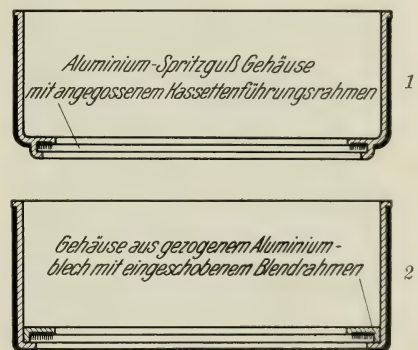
Ausführungsformen des Kameragehäuses mit ringsherumlaufenden Schutzkanten für die Beledung. 1. Eine sehr solide Gestaltung des Gehäuses läßt sich bei einem Minimum von Materialaufwand dadurch erzielen, daß man Aluminium-Spritzguß verwendet; trotz der geringen Wandstärke von 1,5 bis 2 mm ist die Festigkeit eine große und eine Nachbearbeitung der untereinander völlig gleichartigen Stücke überflüssig. 2. Gehäuse für Kameras in niedriger Preislage werden häufig aus dünnwandigem Eisenblech (zirka 0,5 mm) gezogen und mit den übrigen Teilen durch Löten, Schweißen oder Nieten verbunden, bei Verwendung von Aluminiumblech muß die Wandstärke zirka 3 mal so groß sein
